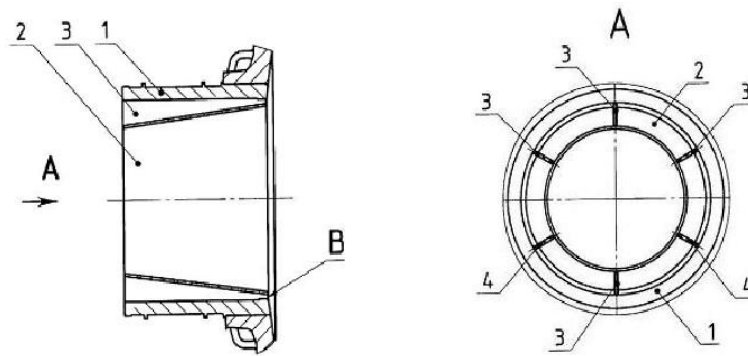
Циліндричний конус цапфи 1, футерувальний патрубок 2, проміжні елементи 3, опорні ребра 4.
